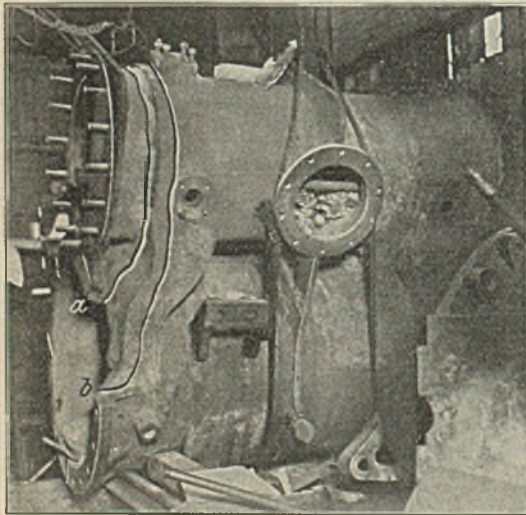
Dampfzylinder von 900 mm Durchmesser mit angeschossenem Kolbenschieber-Gehäuse, 10 t schwer, nach autogener Verschweißung des Hauptbruchstückes.
